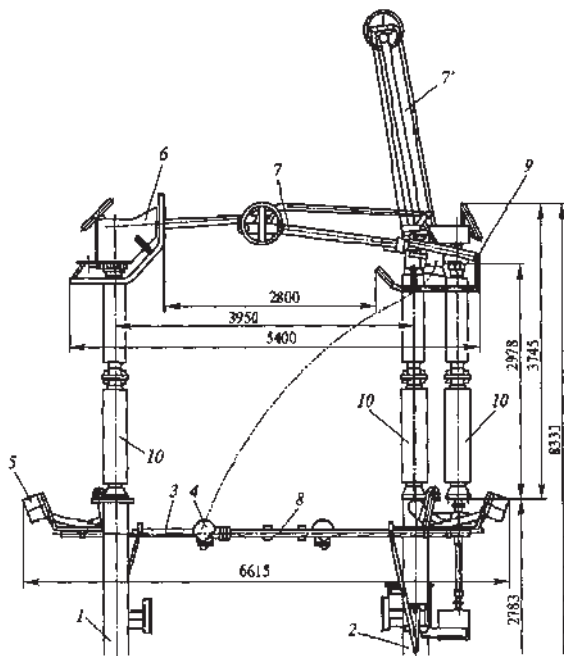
Основні компоненти напівпантографного роз'єднувача: 1, 2 — стійки; 3 — труба; 4 — кожух; 5 — протизаги; 6 — нерухомих контакт; 7 — контактний ніж у включеному положенні; 7' — контактний ніж у відключеному положенні; 8 — заземлювач; 9 — контактний вивід; 10 — ізолюючі колонки
